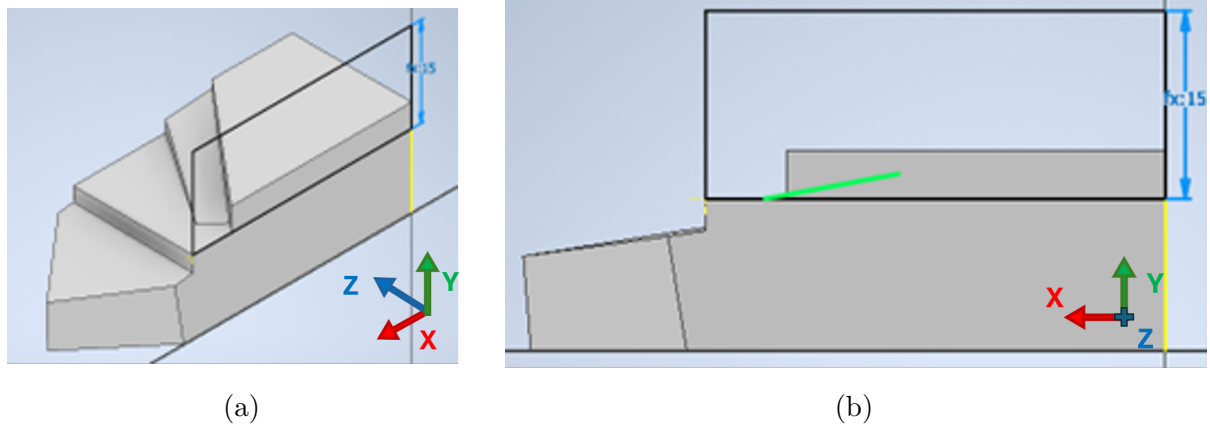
Criação do Esboço 8 e dimensões utilizadas para posicionamento, representado em vista isométrica (a) e em vista frontal (b)
